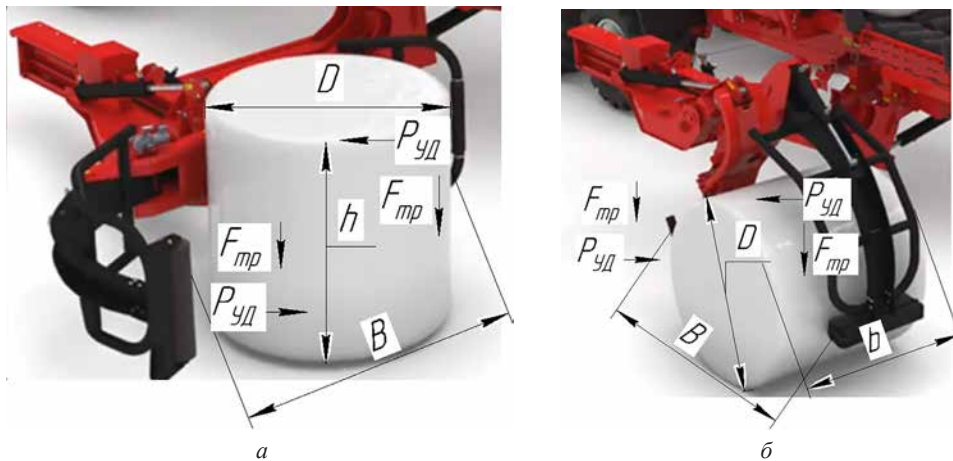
Конструктивно-технологическая схема захвата рулона автоматизированным погрузочно-захватывающим устройством: *а* – захват рулона, расположенного на торцевой поверхности (вертикально); *б* – захват рулона, расположенного на боковой поверхности (горизонтально)
